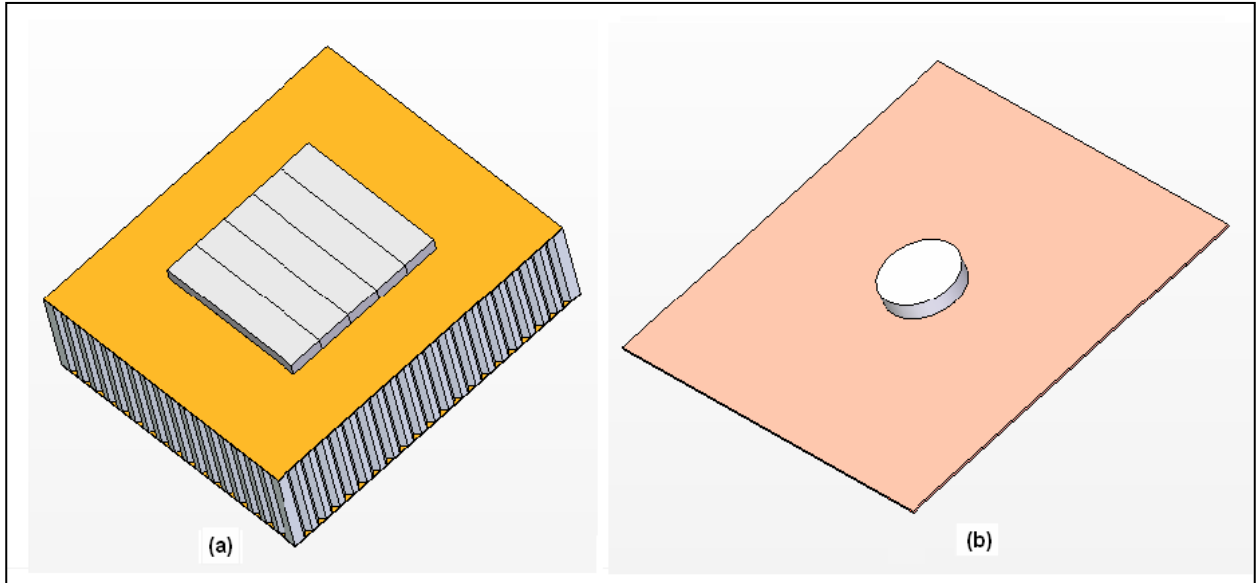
Vista isométrica das montagens das: (a) blindagem 1 e (b) blindagem 3.
